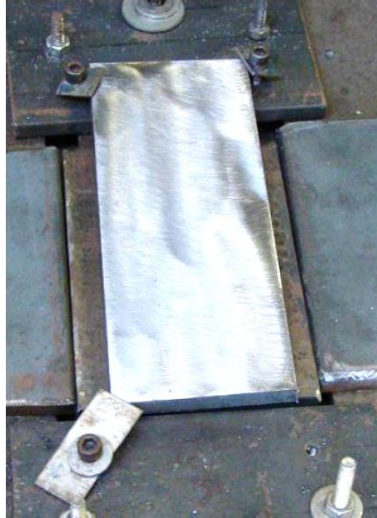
Imagem mostrando a fixação do corpo de prova na mesa de soldagem utilizado nos ensaios cordão sobre chapa
